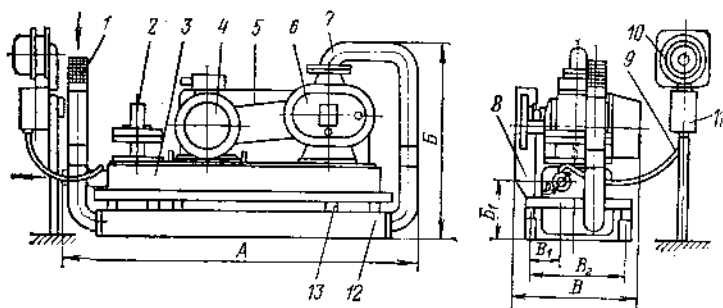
Компрессорная установка с шестеренчатым двухроторным компрессором типа ЗАФ:
